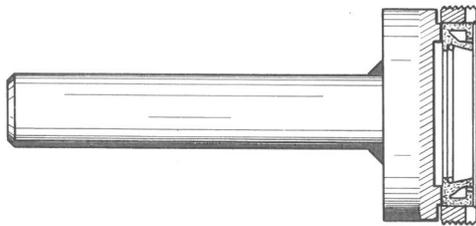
DÉMONTAGE DU MOYEU AVANT
